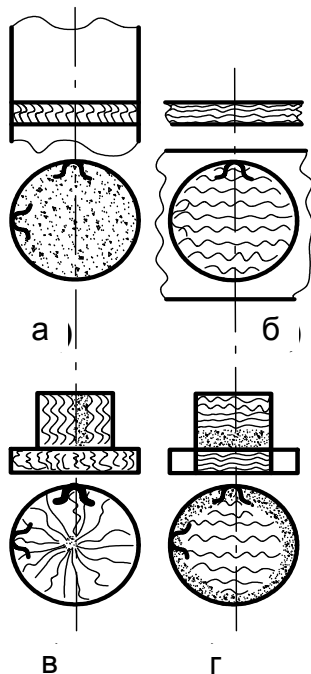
Виготовлення шестерні 1 із заготовки 2 з різним розташуванням волокон: а – з прокату; б – з листового прокату; в – з прутка, осадженого уздовж волокна; г – з прутка, осадженого поперек волокна
